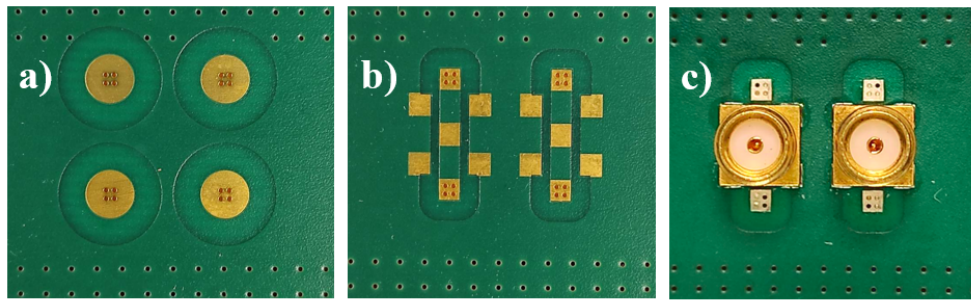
Photographie d'un îlot de 4 applicateurs a) vue de dessus, b) vue de dessous sans connecteur SMA, c) vue de dessous avec connecteurs SMA soudés
